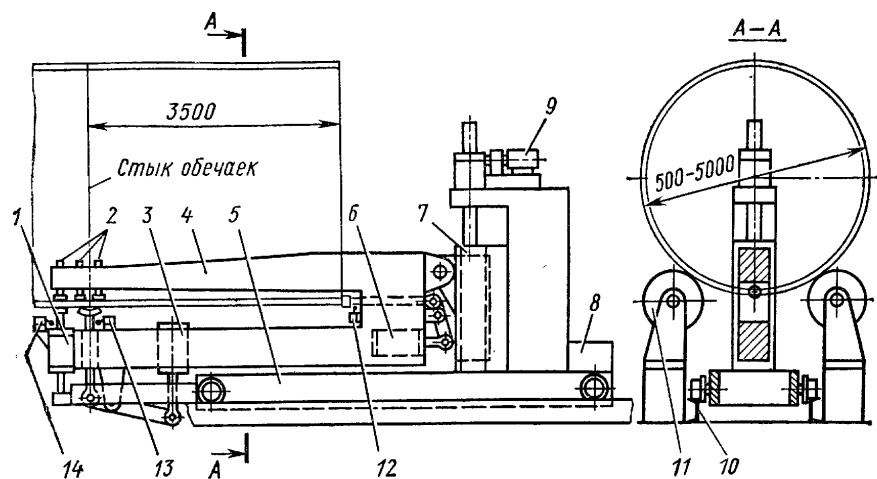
Установка для сборки обечаем по кольцевым стыкам:
